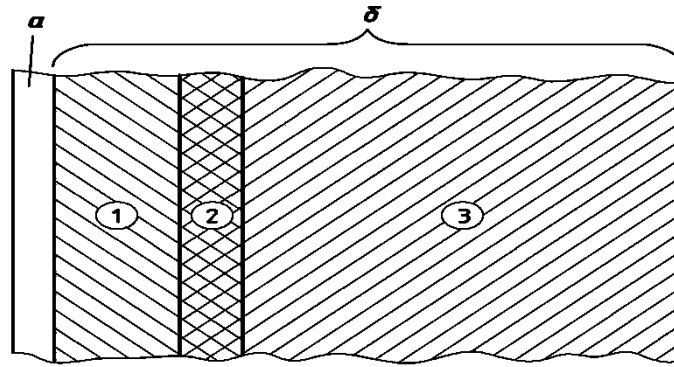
Конструкция цилиндрической части стенок конвертера: а – стальной кожух, б – огнеупорная футеровка. 1 – армирующий слой, 2 – промежуточный слой, 3 – рабочий слой
